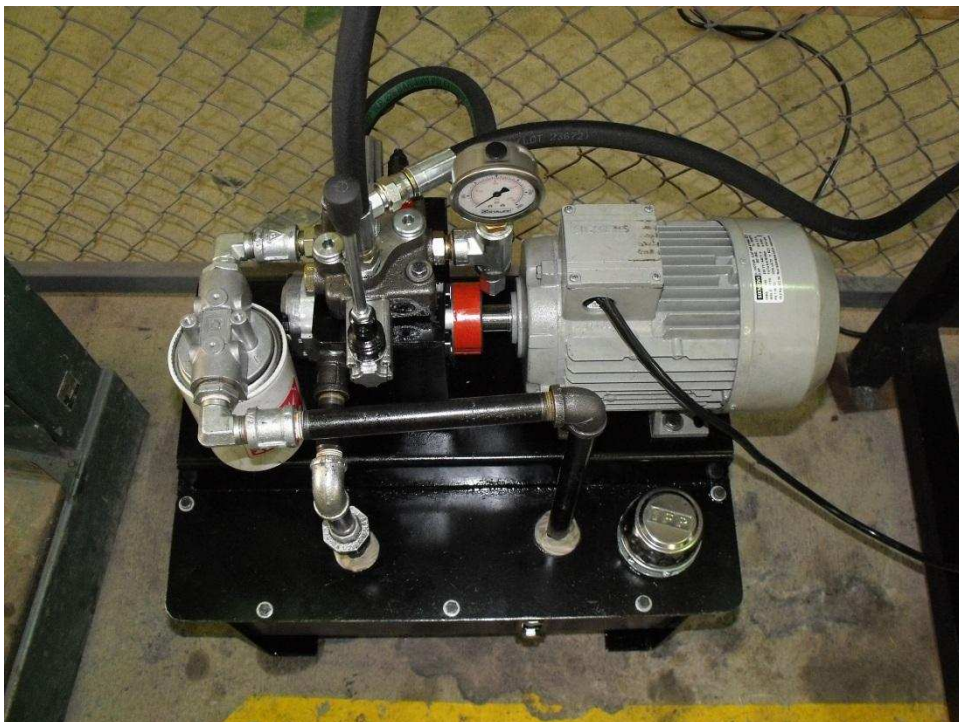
Máquina de ensayos destructivos en juntas soldadas y su sistema hidráulico (ensamble final) 1
